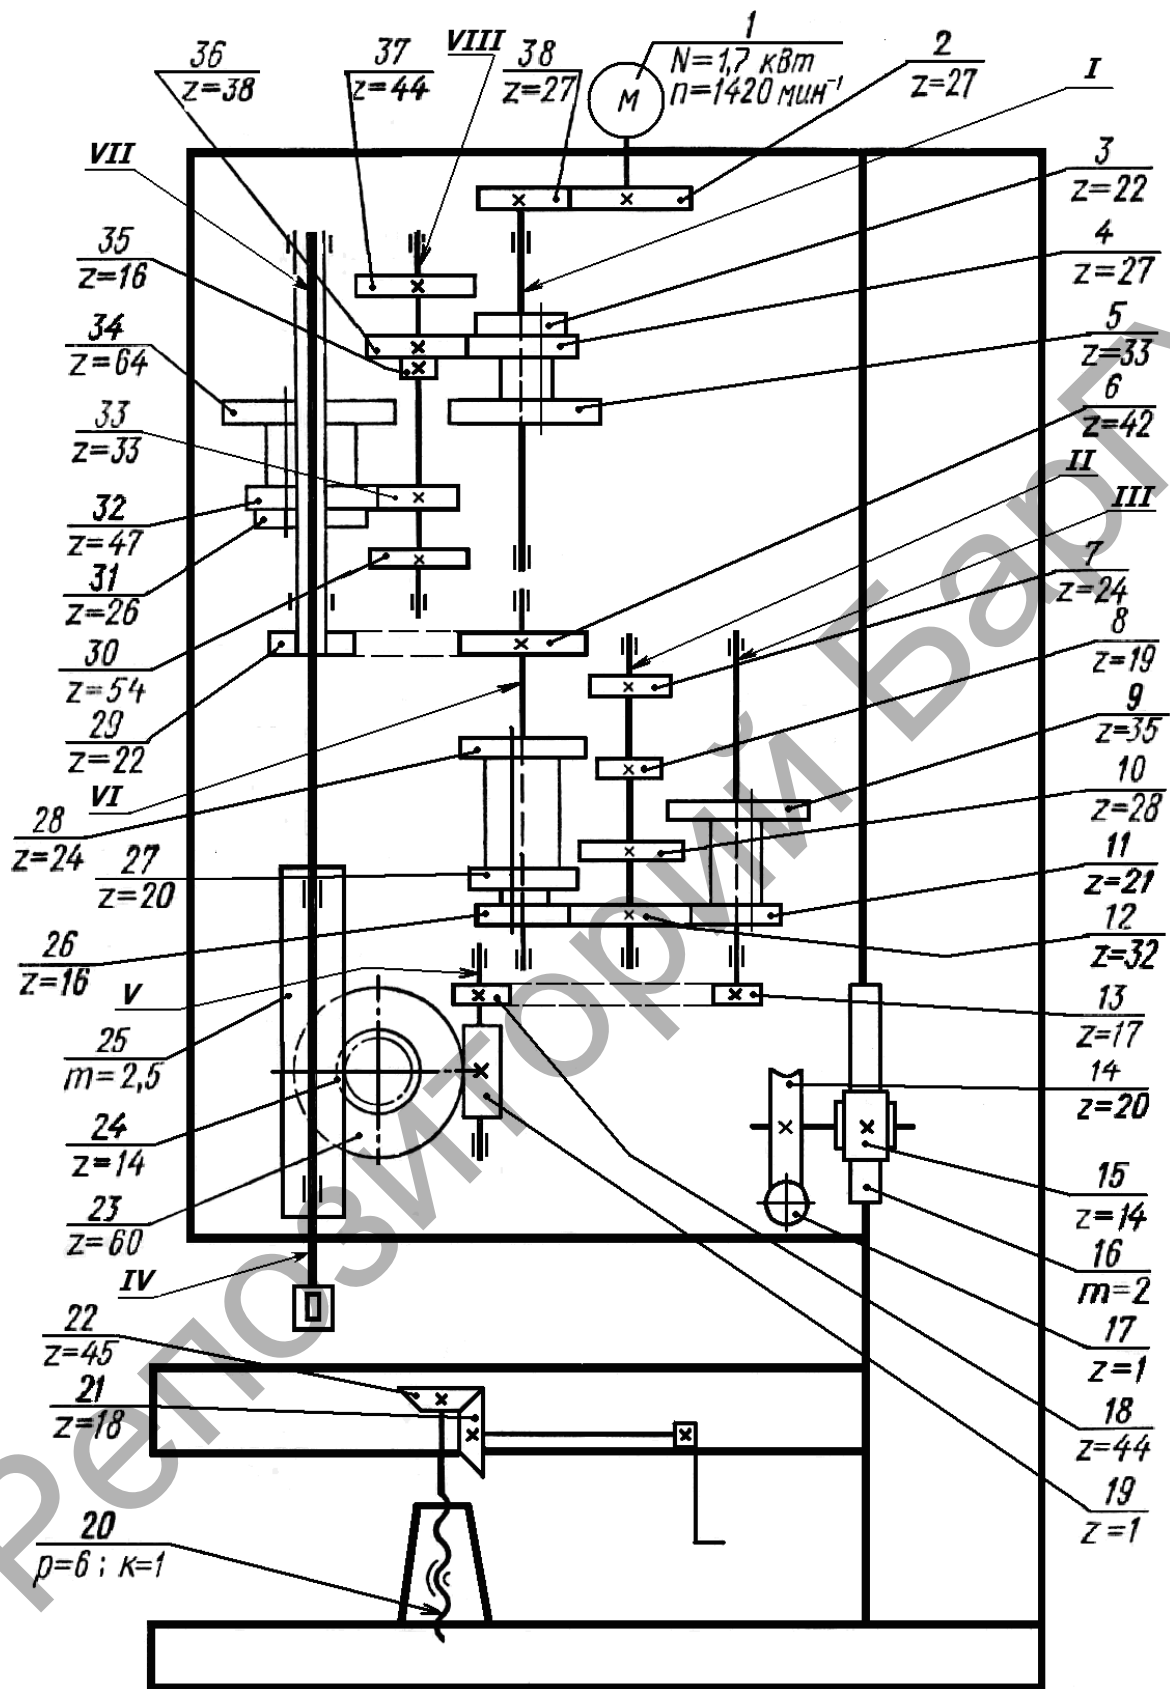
Кинематическая схема станка модели 2Н118
